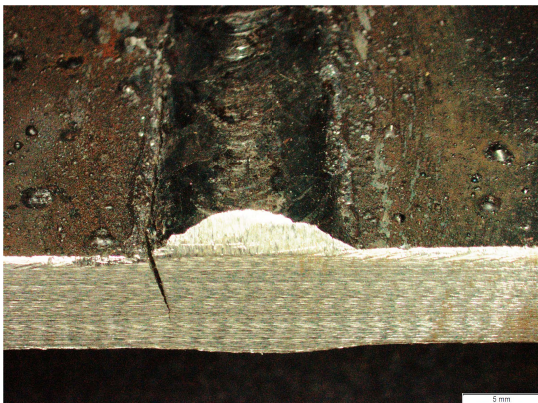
Probe G04-03, Schweißnaht FAT 112, Durchläufer
